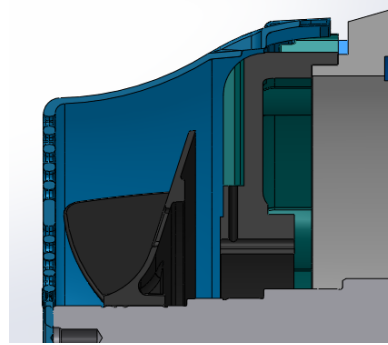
Posição 2 (Ventilador Padrão 420x134, Cota P = 31 mm, Cota H = 28.2 mm, Cota F = 8.54 mm)
